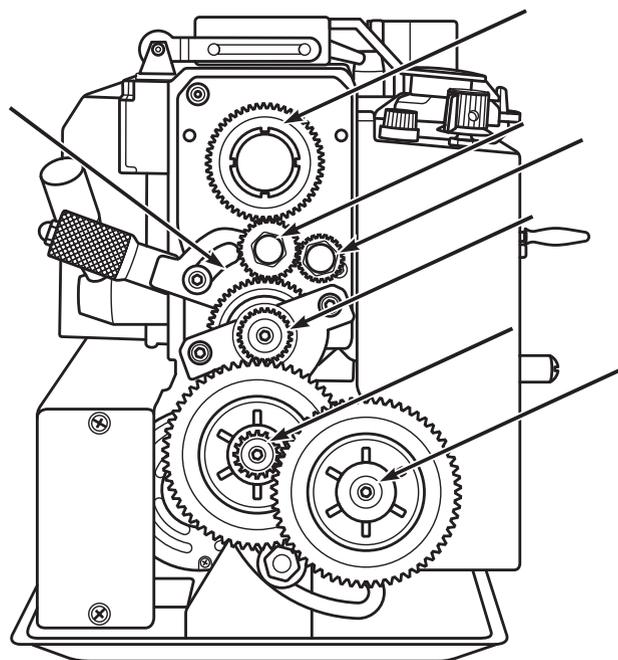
Схема смазки гитары зубчатых сменных колес
